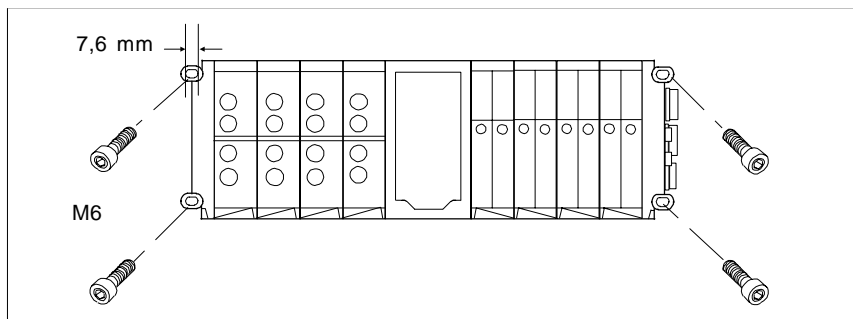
/4 : Montage sur panneau d'un terminal type 03
